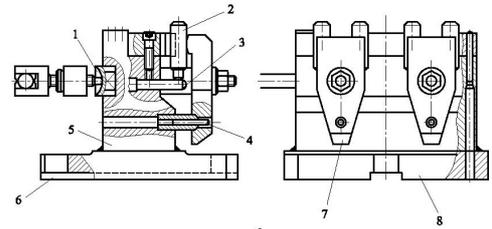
Fräsvorrichtung zum Bolzen schlitzen
